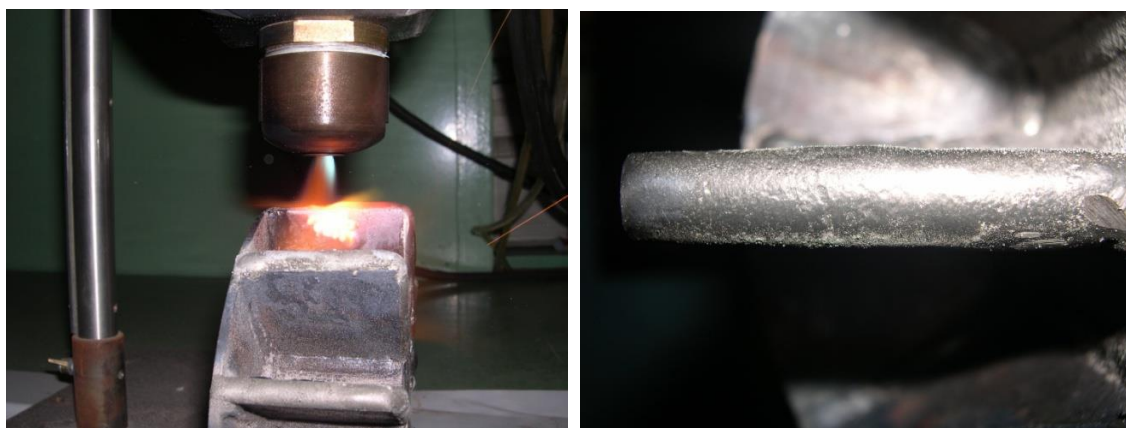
Сверхзвуковая газопорошковая наплавка крыльчатки
